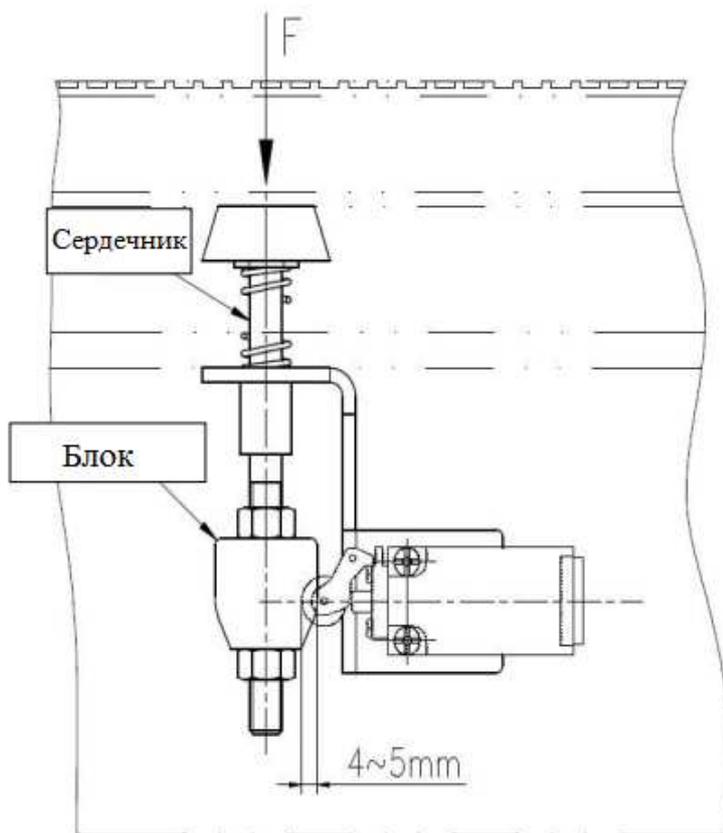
Регулировка защитного устройства напольной плиты.
